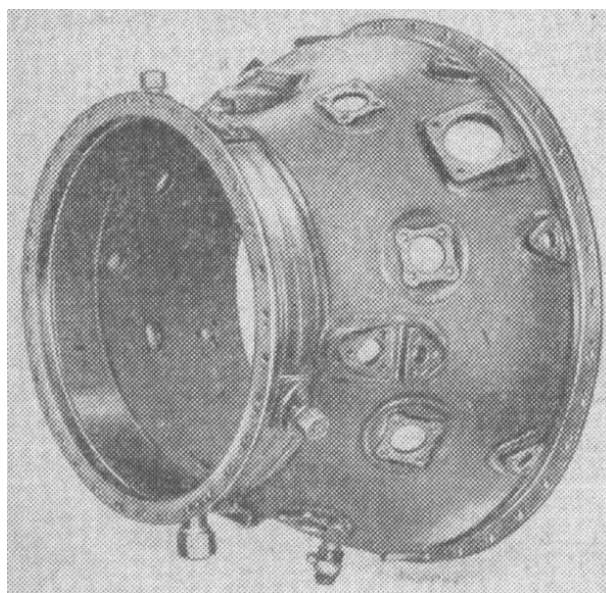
Наружный корпус диффузора (вид спереди слева)
